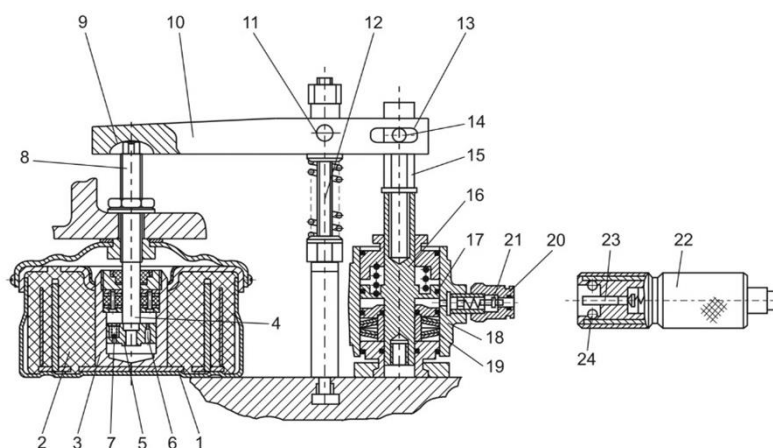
Общий вид виброизолирующего устройства: 1 – основание; 2 – резиновый элемент; 3 – цилиндр; 4 – шток; 5 – поршень; 6 – калиброванное отверстие; 7 – клапан сжатия; 8 – регулировочный винт; 9 – сферическая поверхность лунки; 10 – прихват; 11 – ось; 12 – стойка; 13 – продольный паз; 14 – ось; 15 – опора; 16 – опорный шток; 17 – поршень; 18 – гидроцилиндр; 19 – пружинный аккумулятор; 20 – малая полумуфта; 21 – клапан; 22 – большая полумуфта; 23 – клапанный штырь; 24 – шарики
